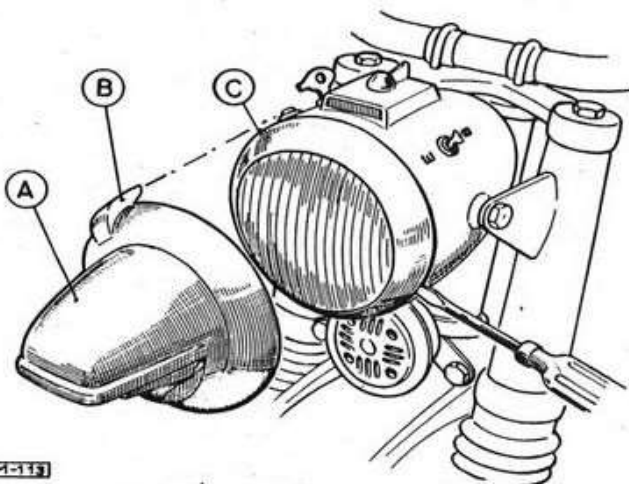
Montaggio della maschera di oscuramento sul proiettore.
